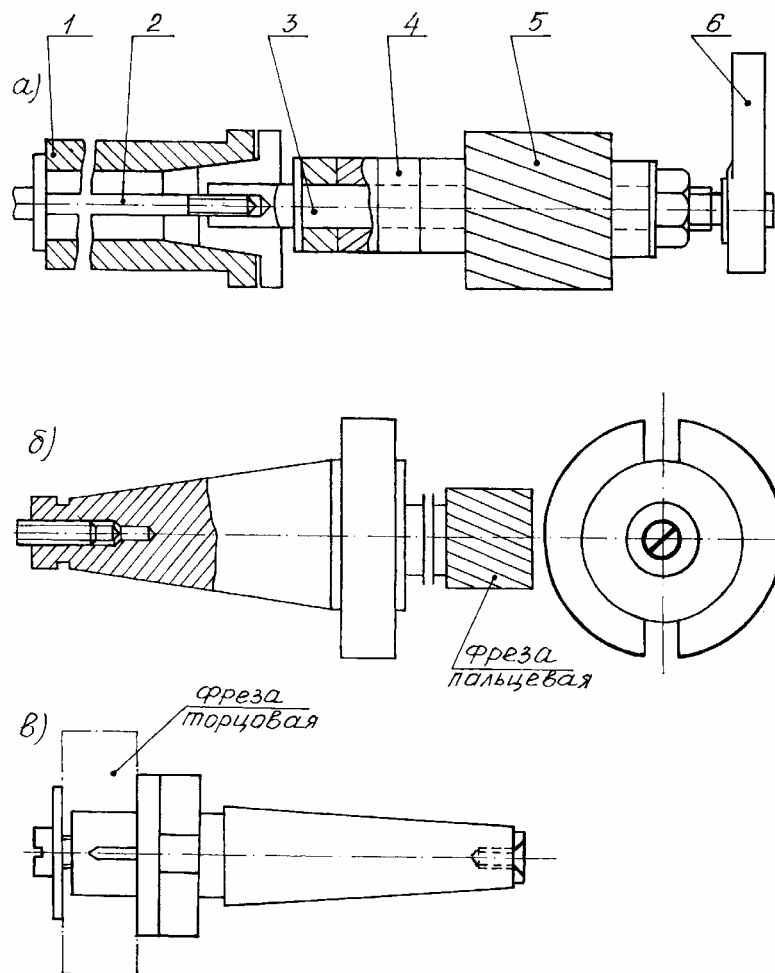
Схемы крепления инструмента на фрезерных станках:
